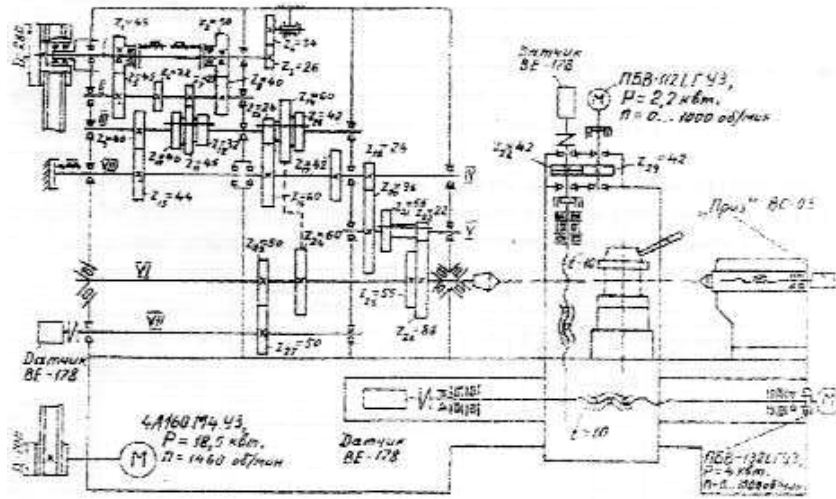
Кинематическая схема токарного патронно-центрового станка 1М63БФ30С1 с ОСУ
